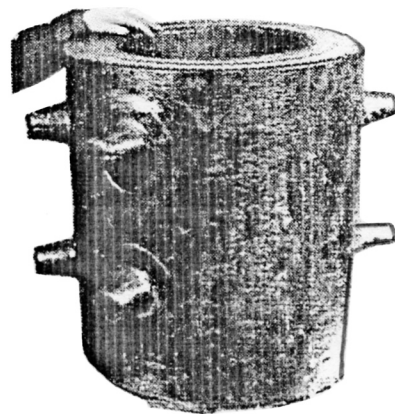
Электрошлаковая отливка с патрубками, сформированными в процессе ее выплавки
